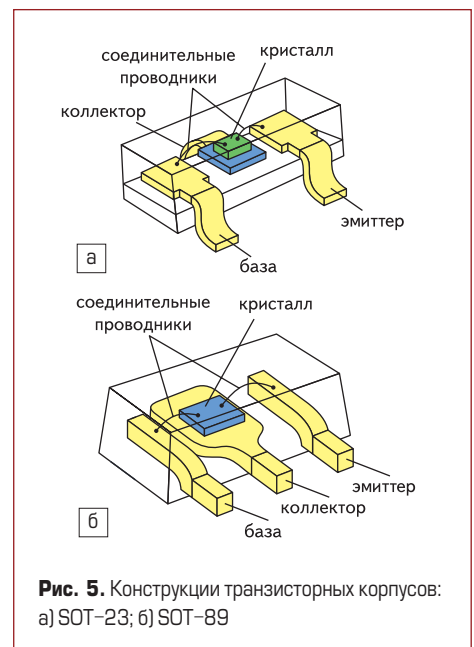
Конструкции транзисторных корпусов: а) SOT-23; б) SOT-89
